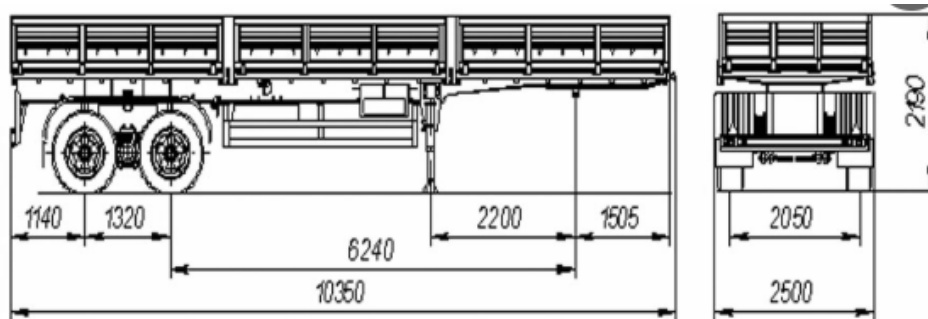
Загальний вигляд та схема напівпричепи типу НЕФАЗ-9334-0000020
